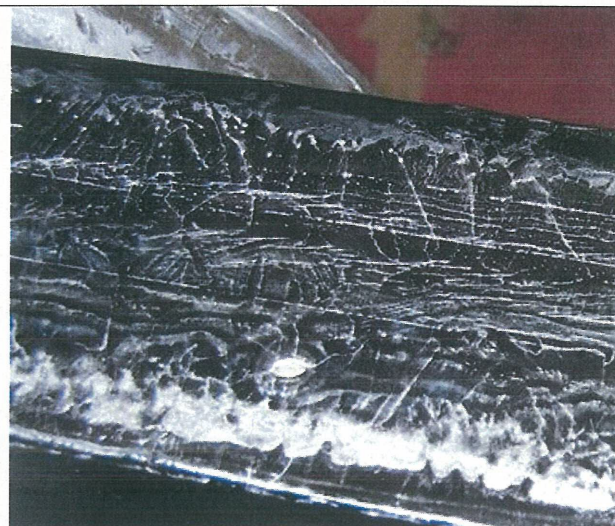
Частица футеровки размером 2 мм на поверхности заготовки
